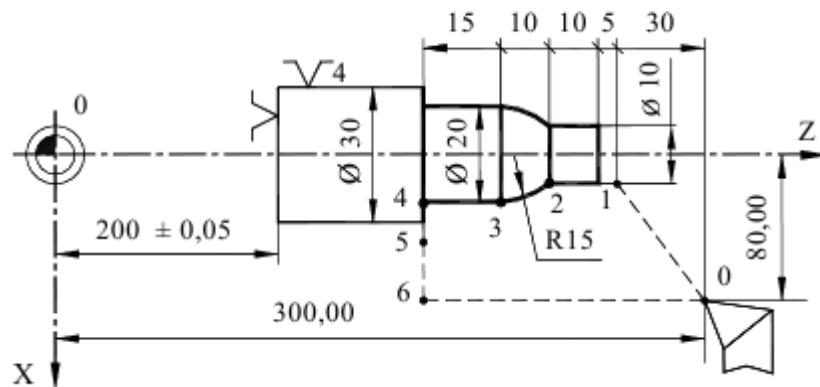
Траєкторія руху різця при токарній обробці заготовки.
